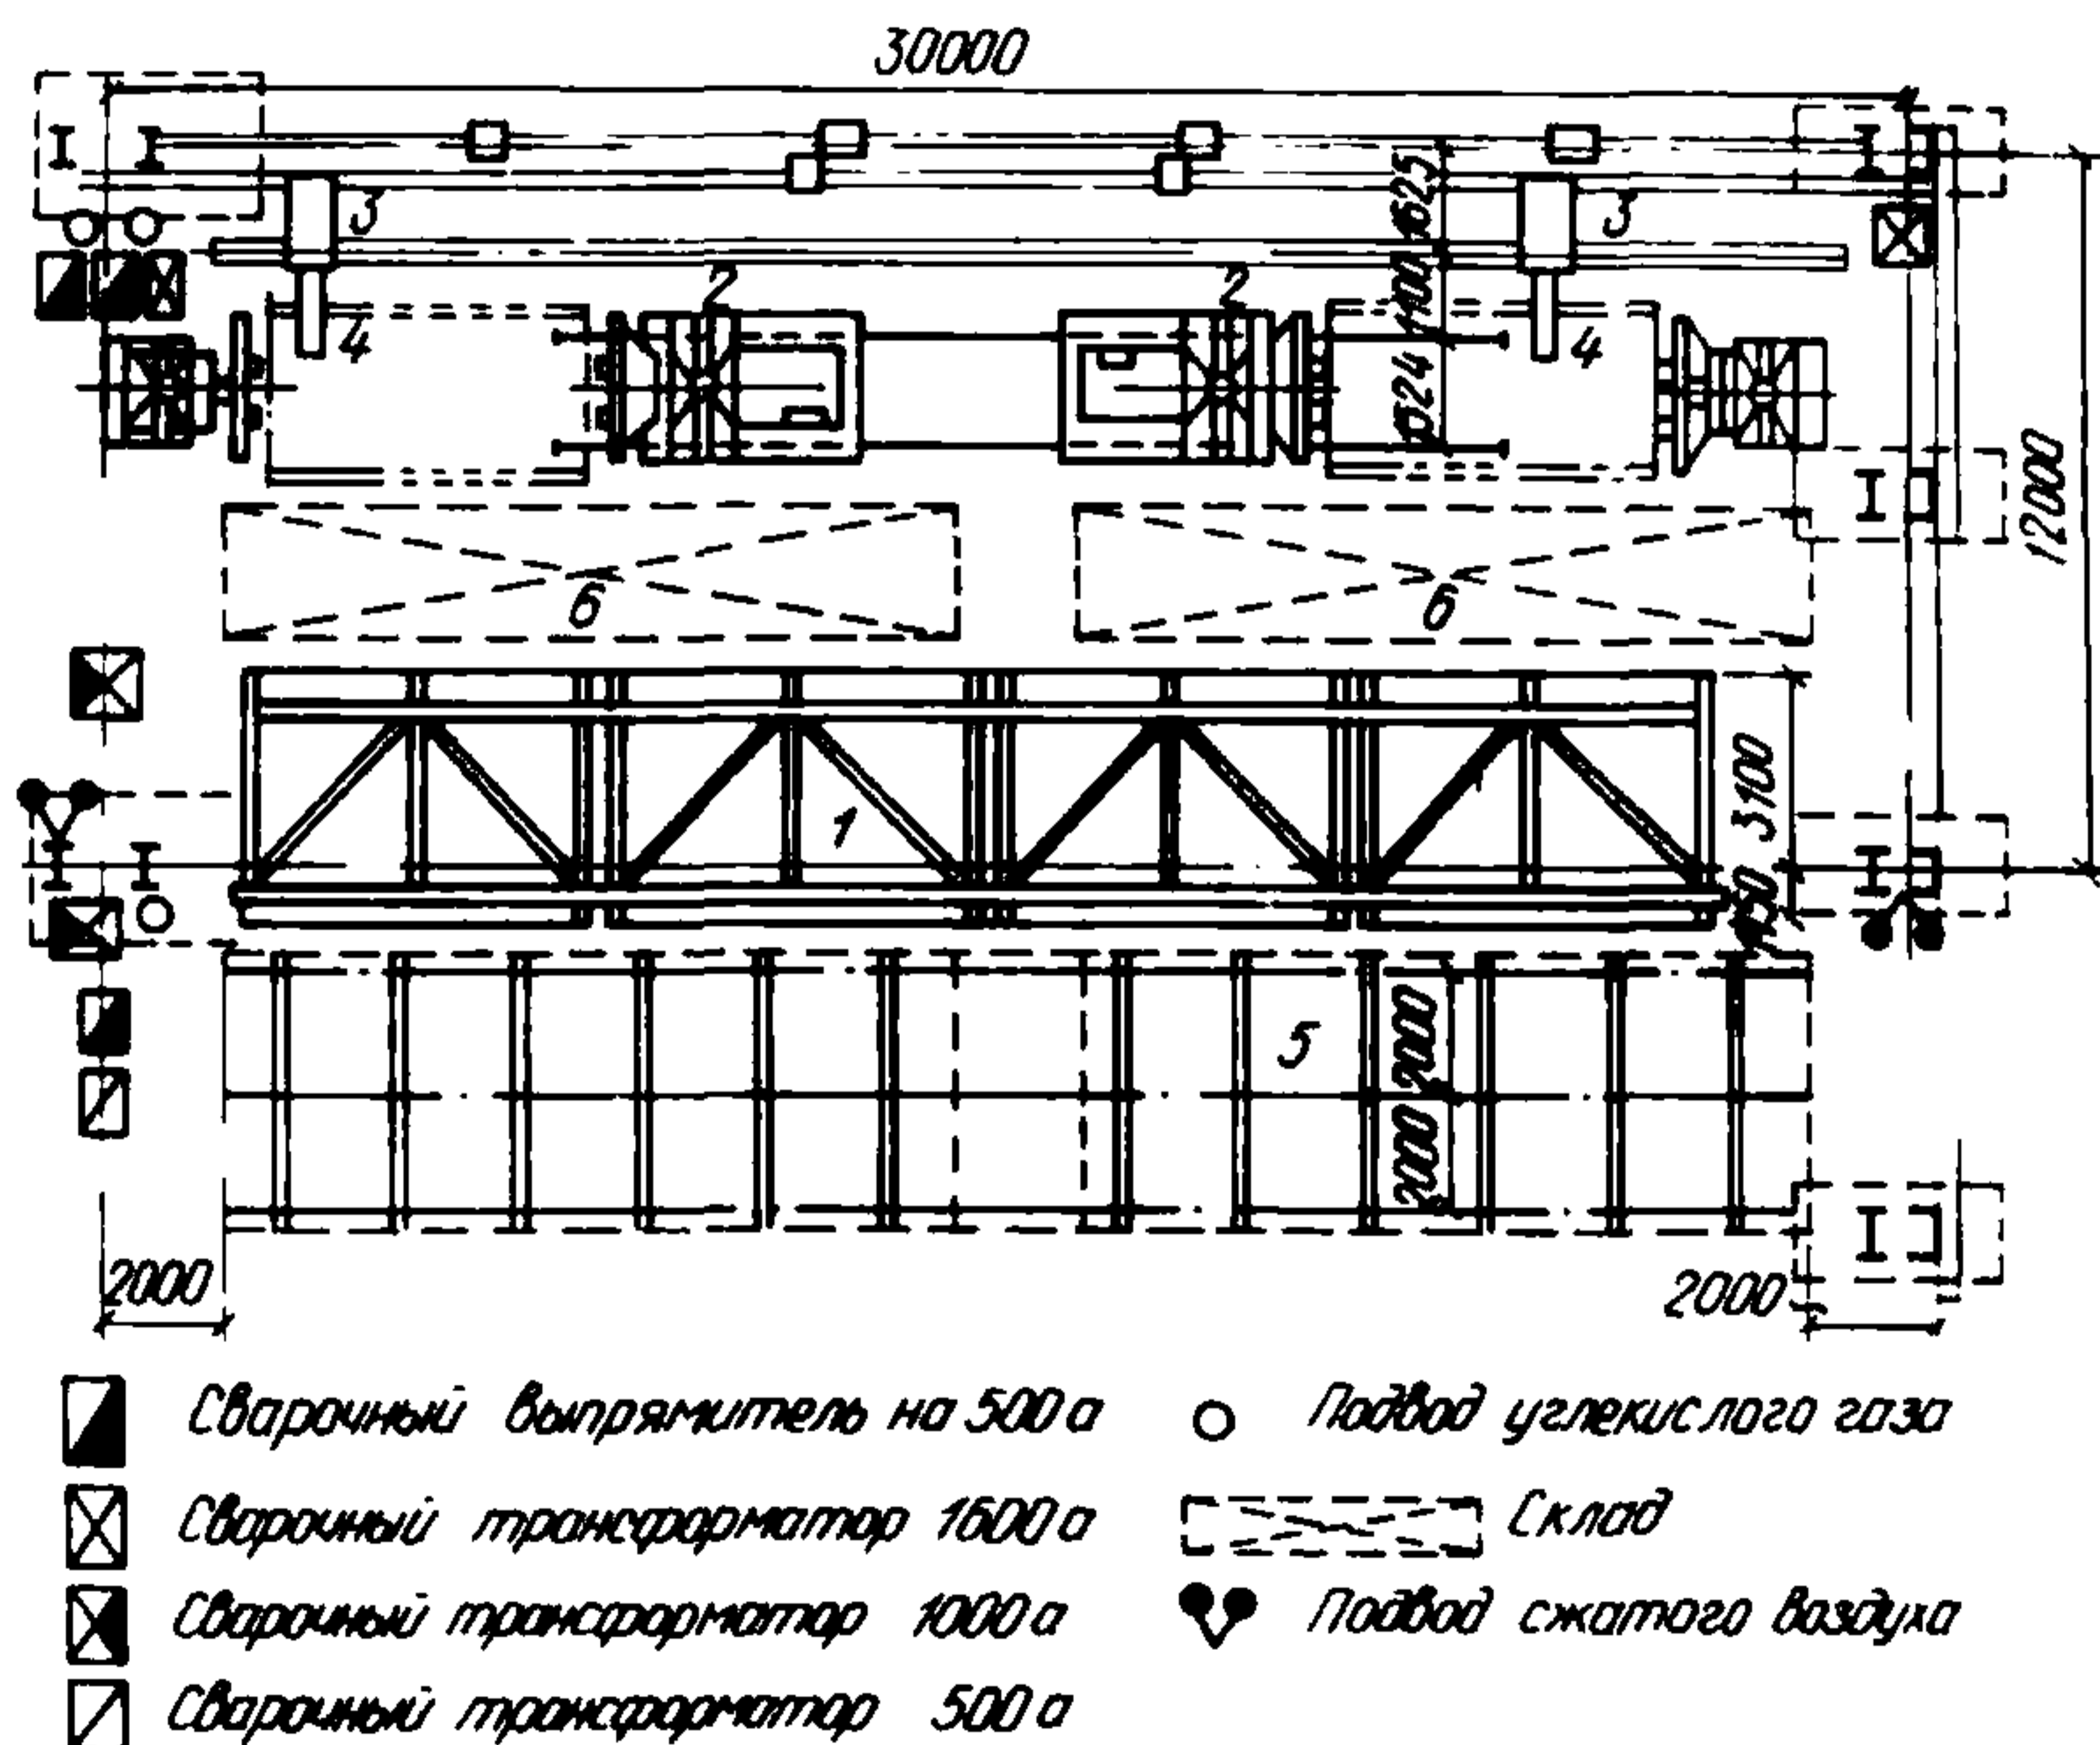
Планировка участка сборки и сварки стержней двутаврового сечения (сварка с использованием велотележки)
